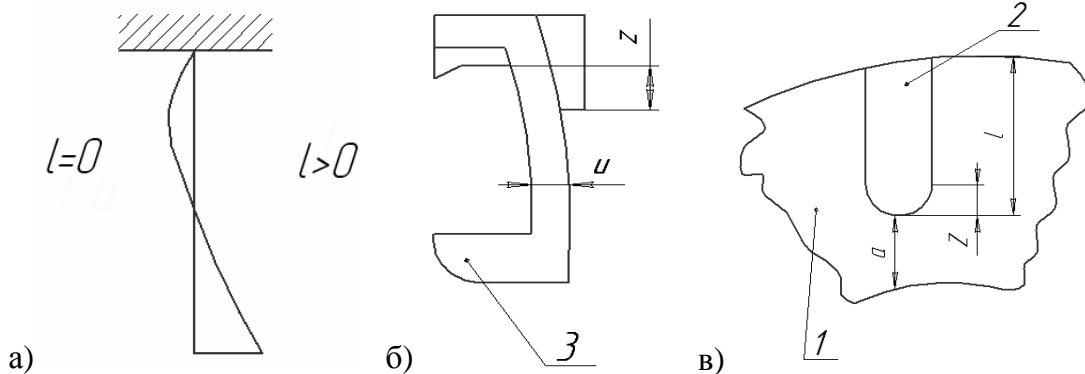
Схема деформации подшипникового щита: 1 – щит, 2 – технологический прилив (ребро жёсткости), 3 – подшипник, ΔZ – размер усталостной трещины, u – толщина стенки щита
